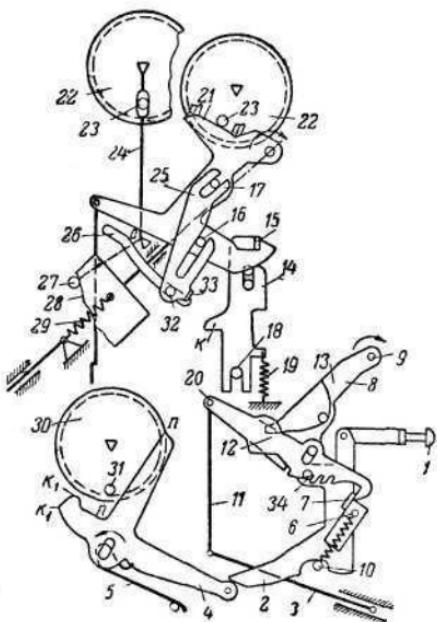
Схема шторного затвора фотоаппарата «Спорт»
